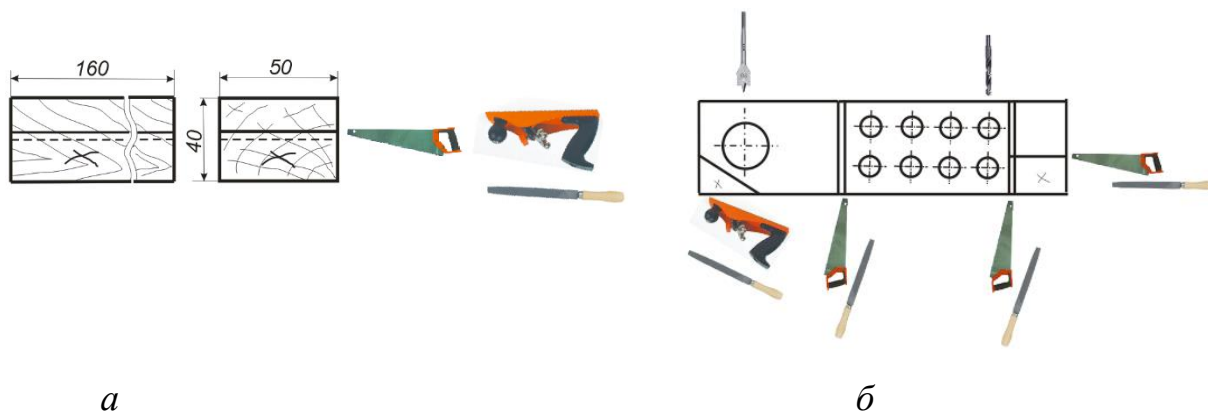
а – продольная разметка и разделение детали; б – разметка и последующая обработка деталей на заготовке.
